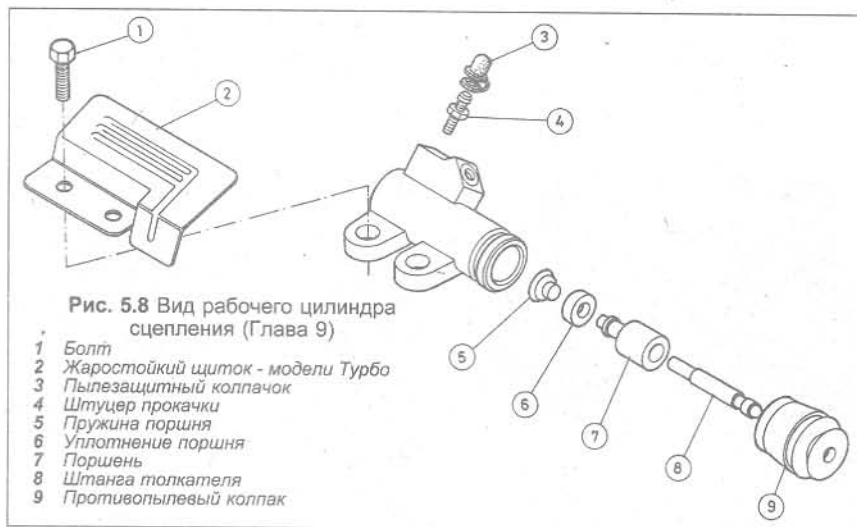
Вид рабочего цилиндра сцепления (Глава 9)
